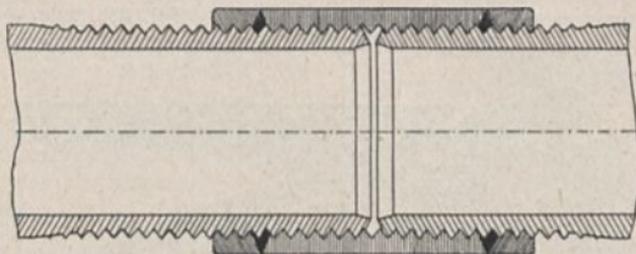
Rohrverbindung durch Muffen mit zylindrischem Gewinde, mit Dichtung durch Packung.
